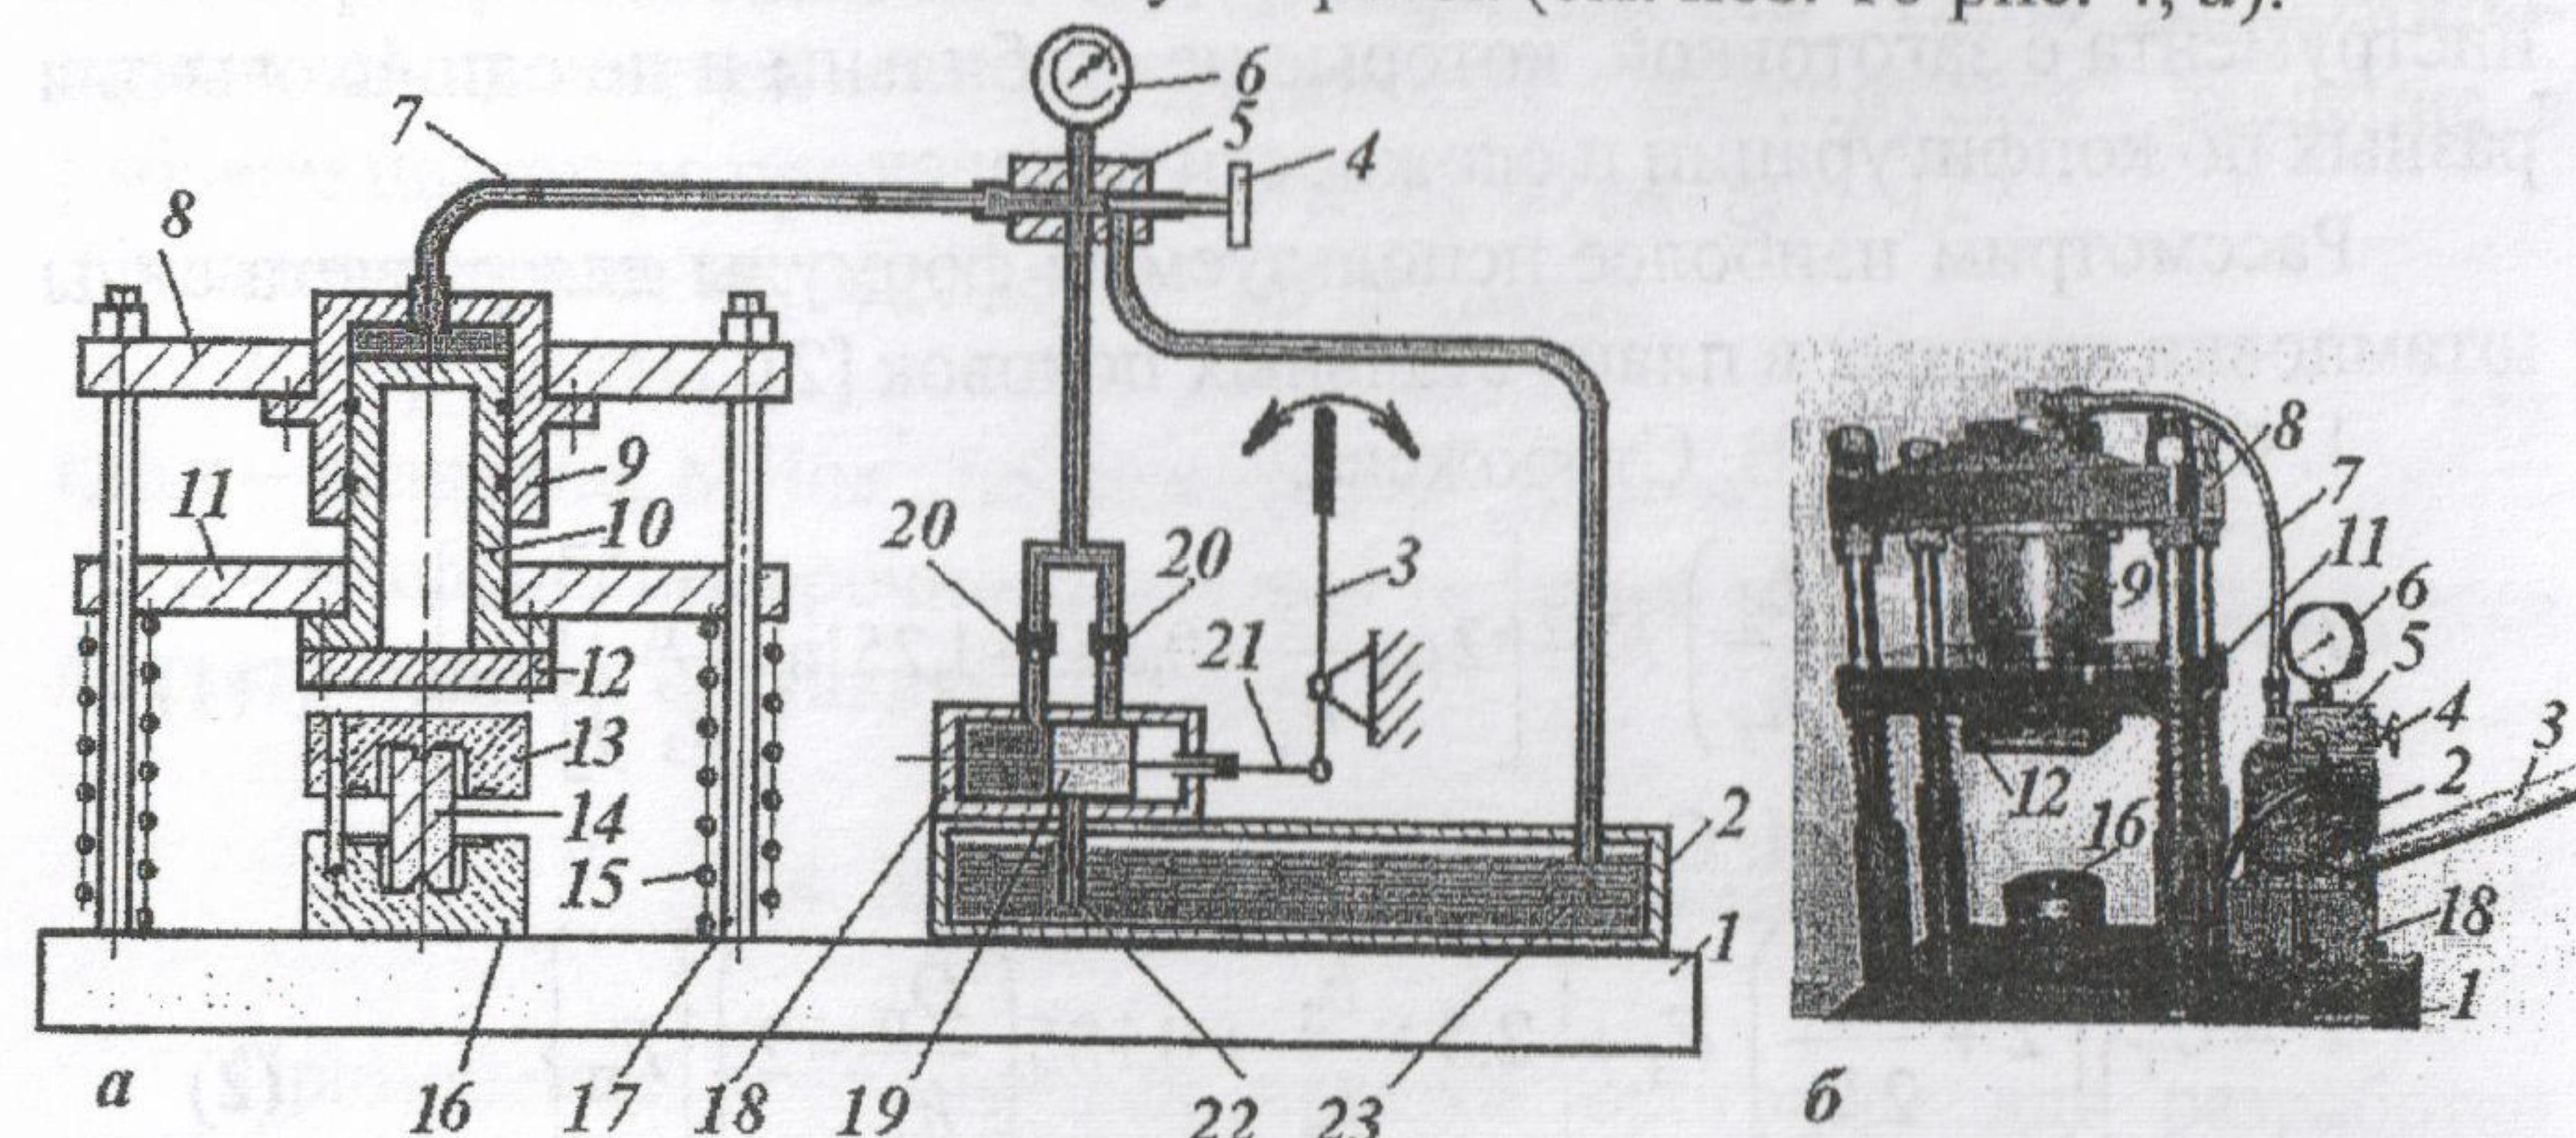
Ручной гидравлический пресс для объемной штамповки:
